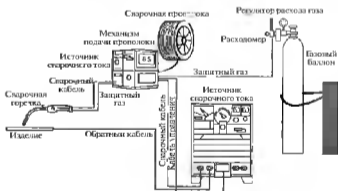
Установка для полуавтоматической сварки в защитном газе
